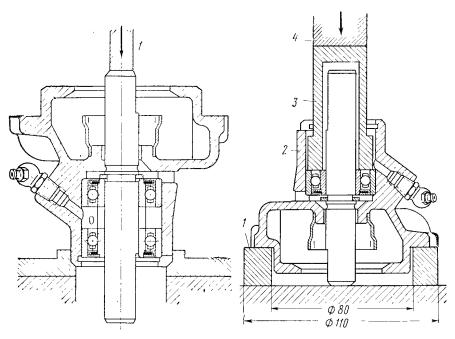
Выпрессовка валика водяного насоса: 1 — плунжер пресса
